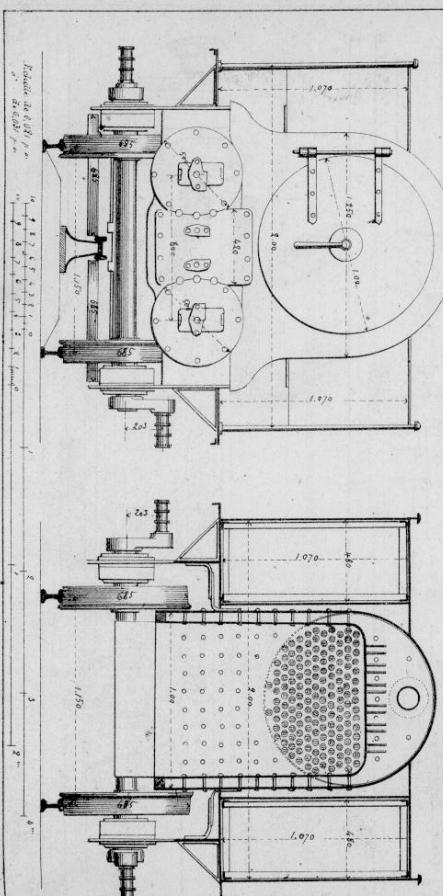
Elevation, coupe longitudinale à 0.021 p.m.
